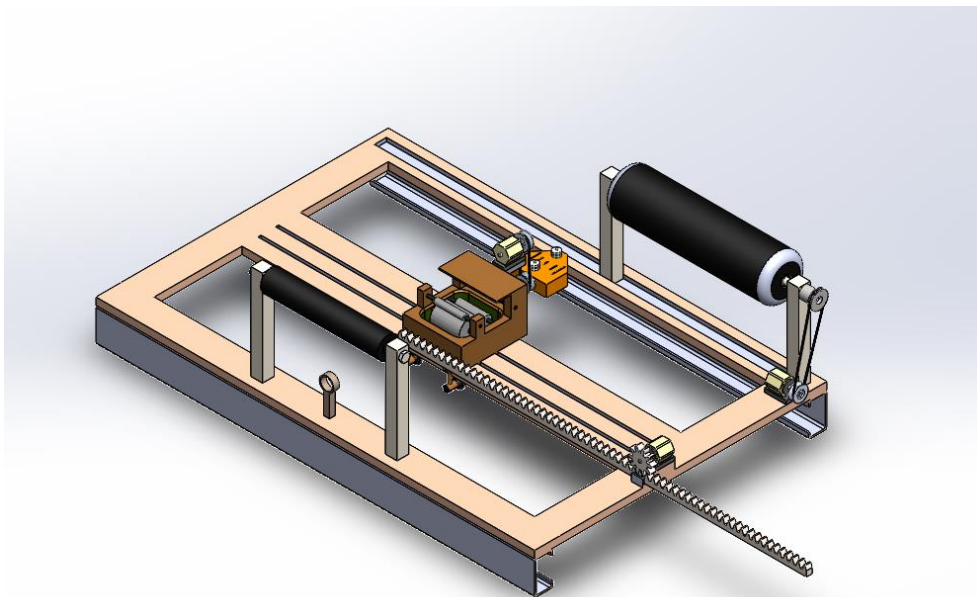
Máquina Filament Winding vista isométrica. Autor
